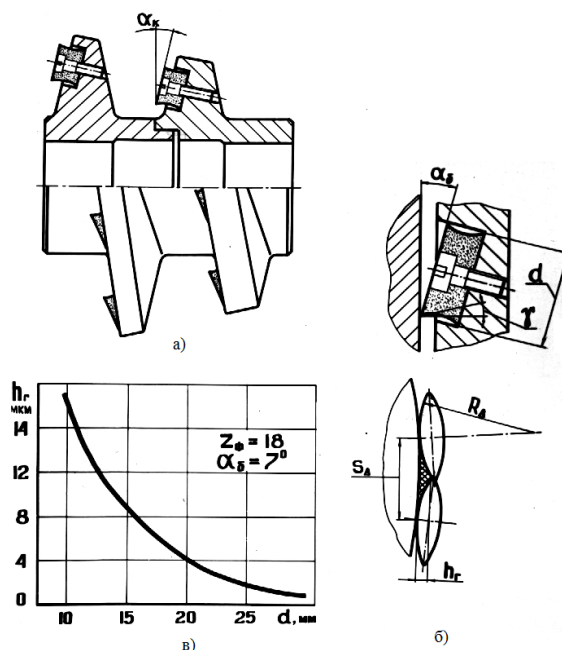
Черв'ячна фреза з роздільною схемою формоутворення з поворотними непереточуваними різальними елементами – вальцями; а – загальний вигляд правого корпусу фрези; б – утворення гребінця нерівності в процесі обкатування зуба колеса; в – залежність висоти нерівностей від діаметру різального елемента – вальця
